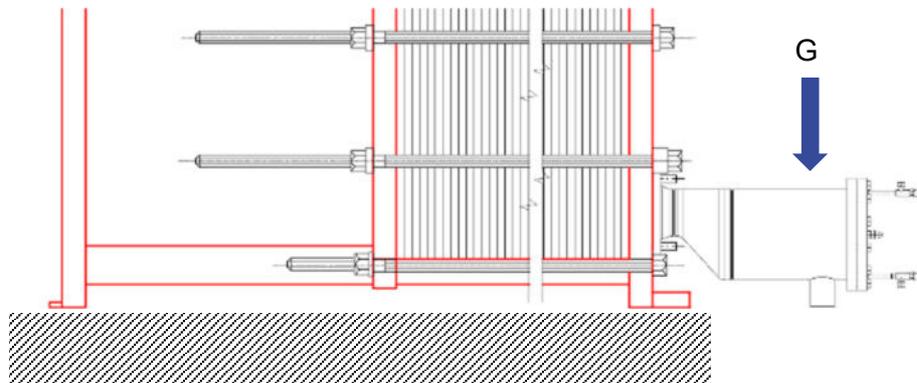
Anschluss eines HS-Schwimmerreglers in Flanschausführung
